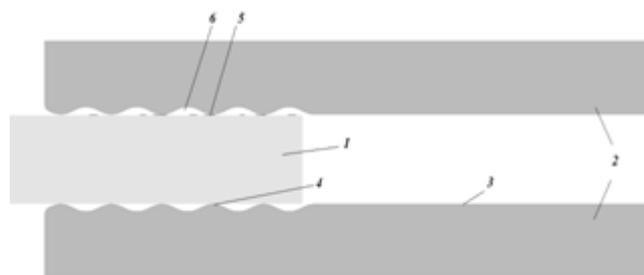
Обжатие заготовки в штампах с комбинированной рабочей поверхностью
